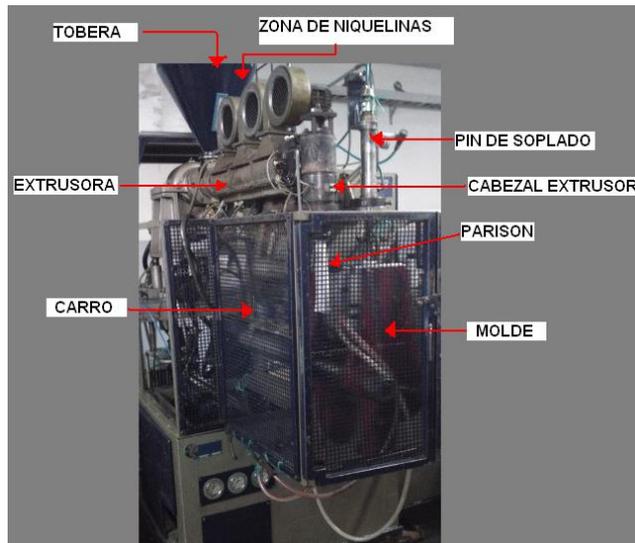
Vista de las partes principales de una máquina de extrusión soplado marca MAGIC.
